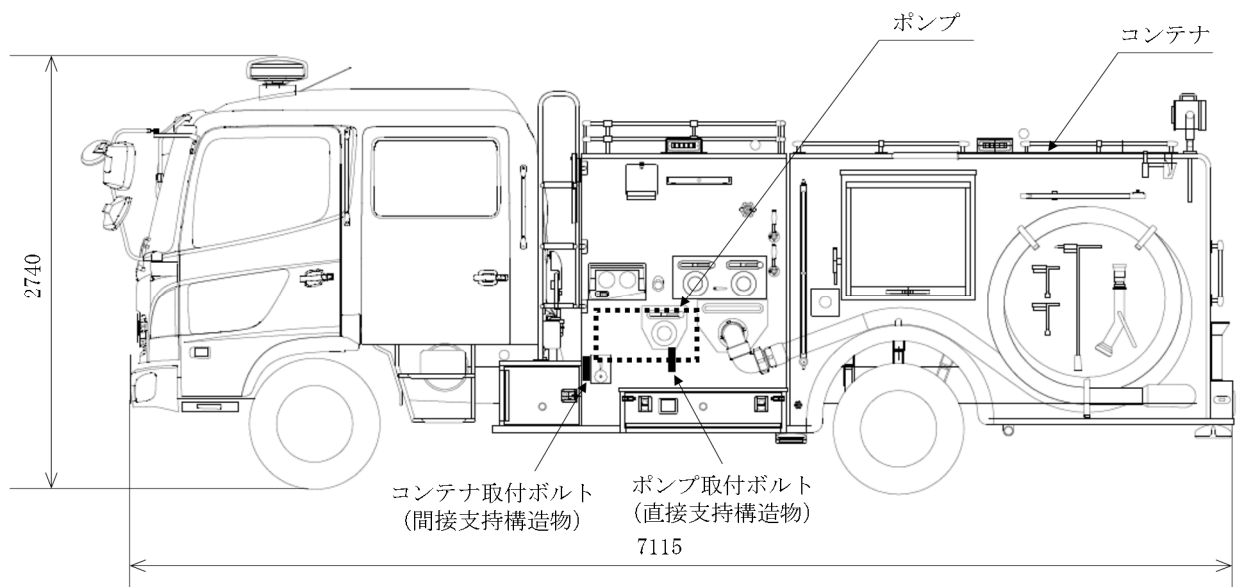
可搬型代替注水ポンプ (A-1級) の構造図 (単位 : mm)
